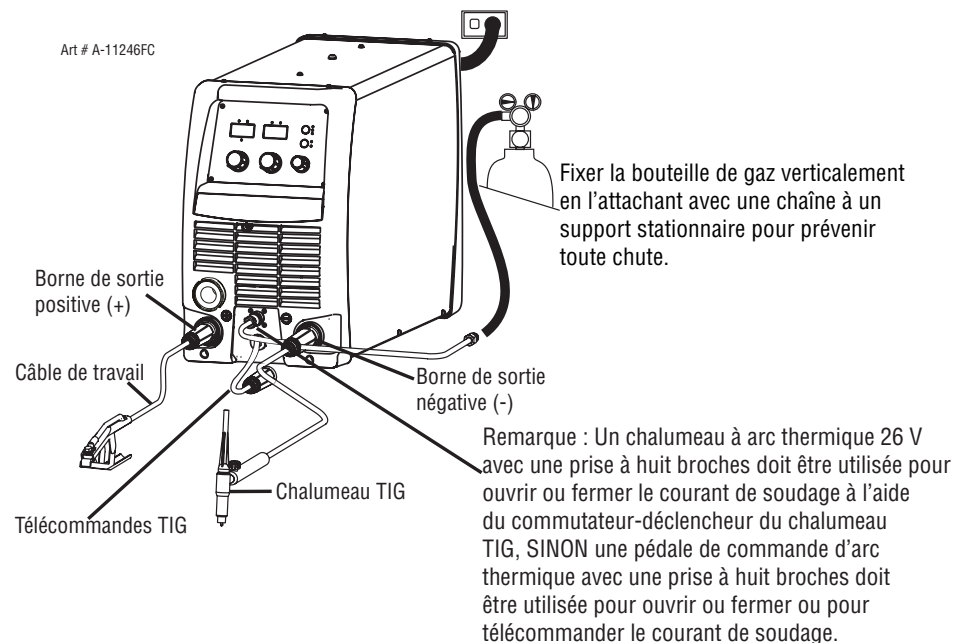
Présentation de la préparation en vue du soudage TIG
